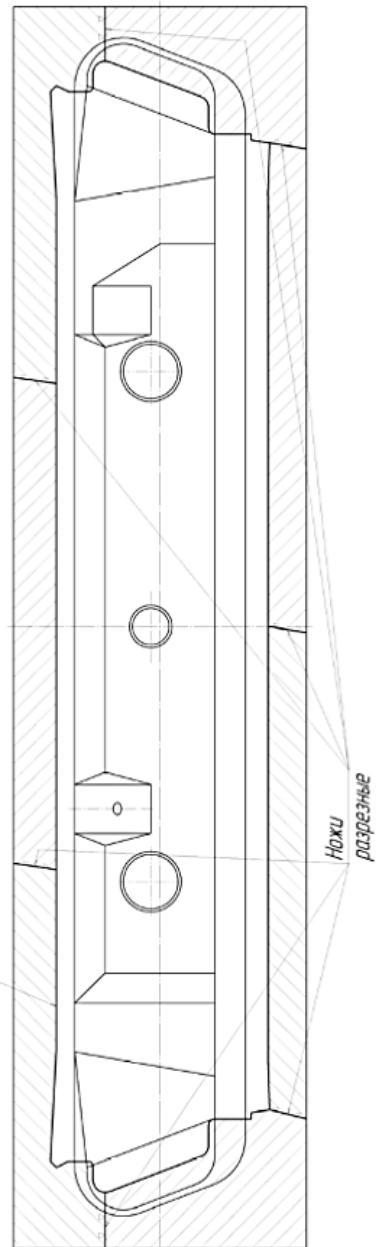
Резка карточек и заготовок (предварительный вариант)
